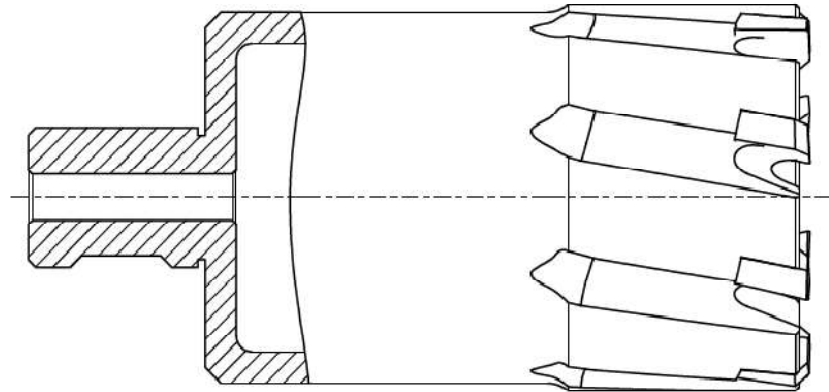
Корончате свердло з твердосплавними пластинами Karnasch
